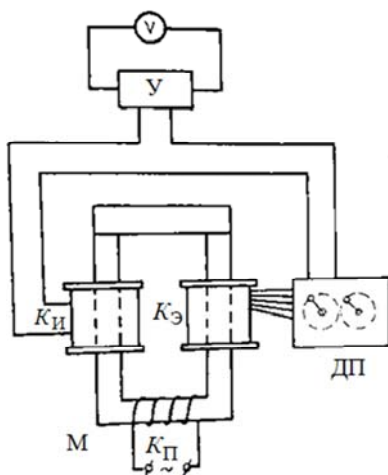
Схема установки для проверки обмоток на короткозамкнутые витки и измерения числа витков
